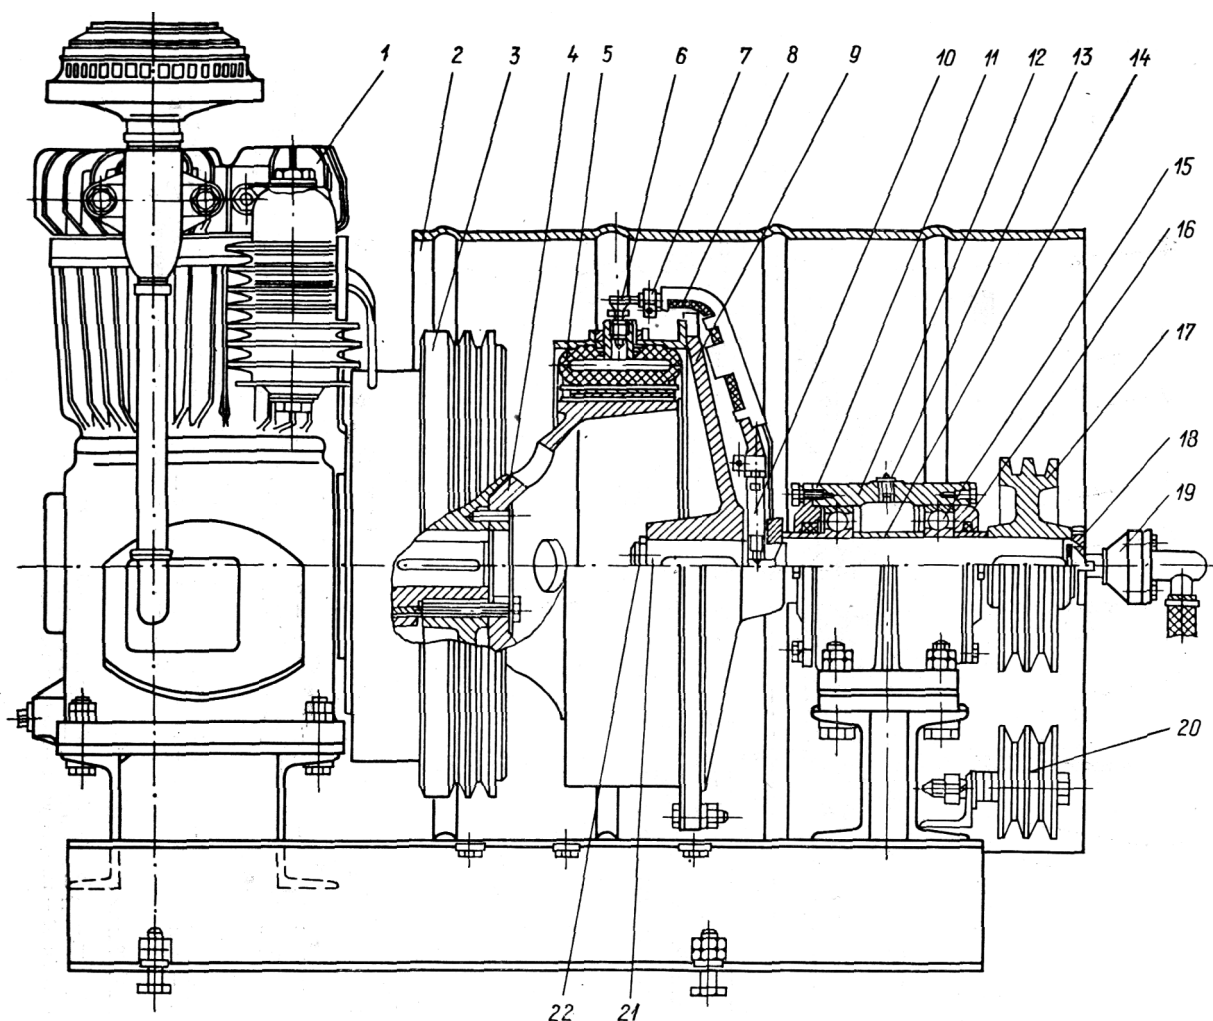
Установка компрессорная установки подъемной с тартальным барабаном
